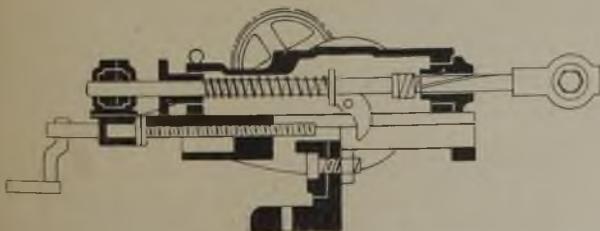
Schematischer Längsschnitt durch die Handstoßbohrmaschine der Jackson Drill Co.
